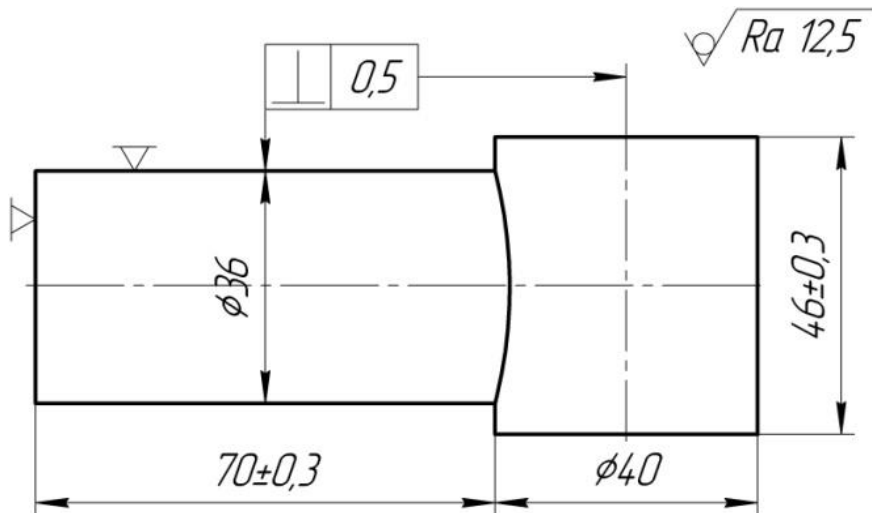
Ескіз заготовки «Вилка тяги»
